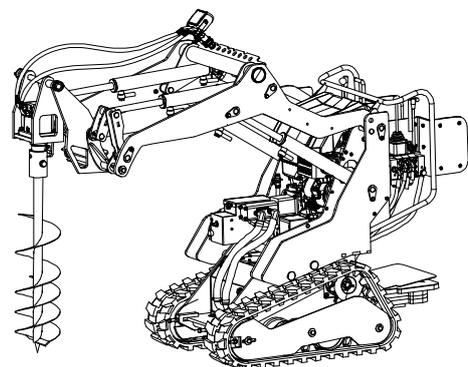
mit Erdbohrer, hydraulisch 5MT2503
